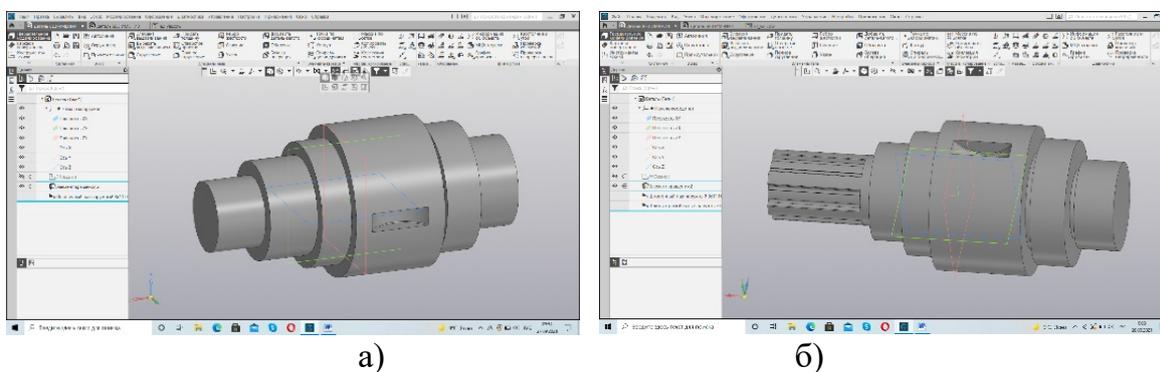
Шпоночный паз на чертеже вала а) и построение шлицев на чертеже вала б)
